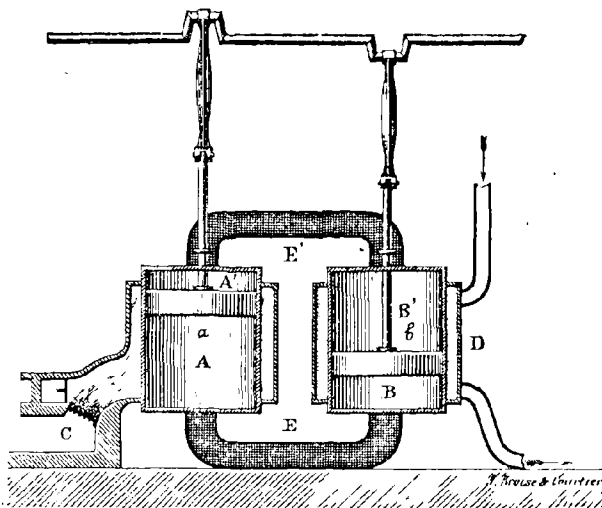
Machine à air chaud de Franchot (coupe verticale).
